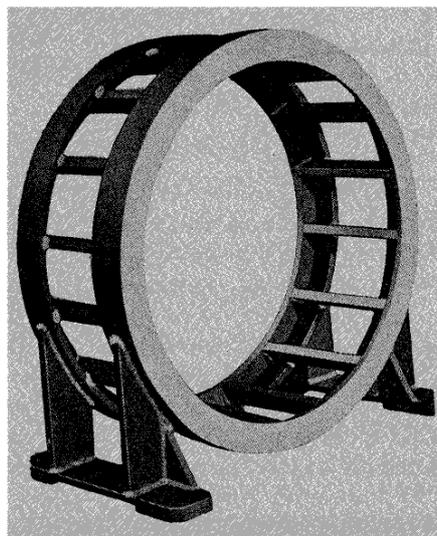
Carcasse d'alternateur soudée.
